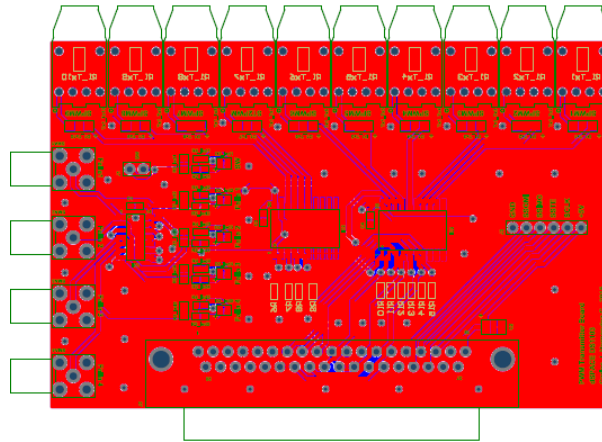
Diseño PCB de la Tarjeta Transmisora de Señales Ópticas.
